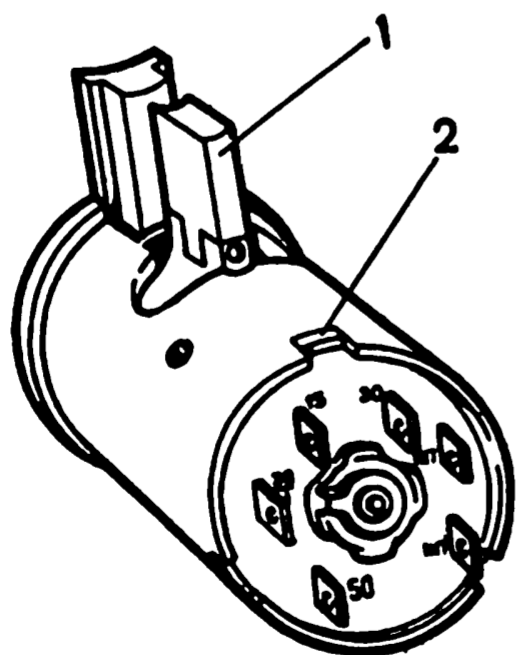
Вид на контактную часть выключателя зажигания: 1 - запорный стержень; 2 - широкий выступ контактной части
